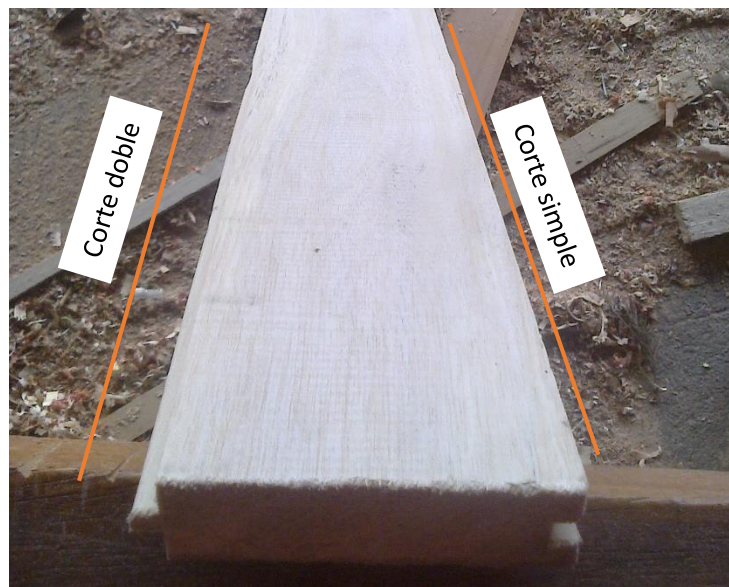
Probeta con ensayo de moldurado con corte doble y simple
